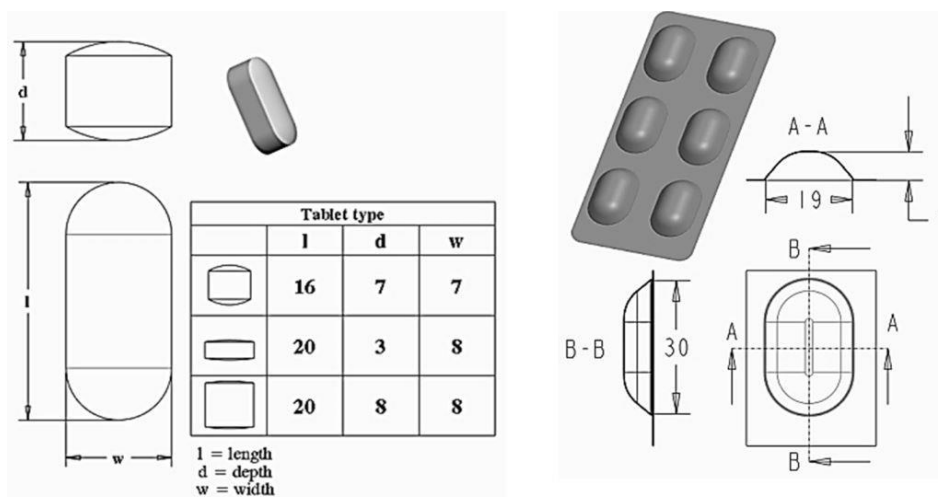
Figure 4-16 placebo tablets and blister – dimensions
